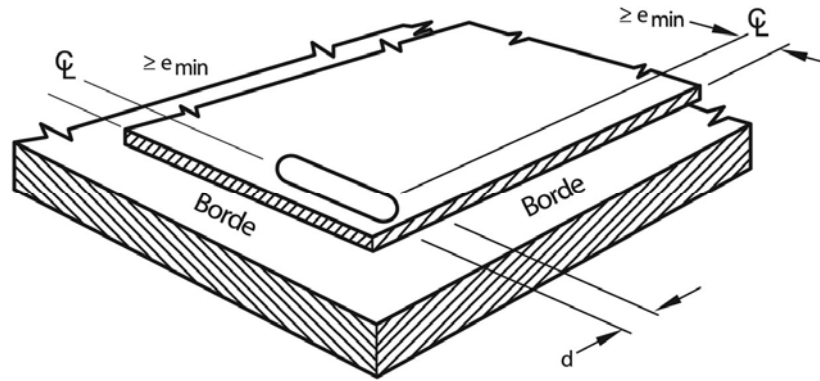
Distancias al borde para soldadura de ranura
